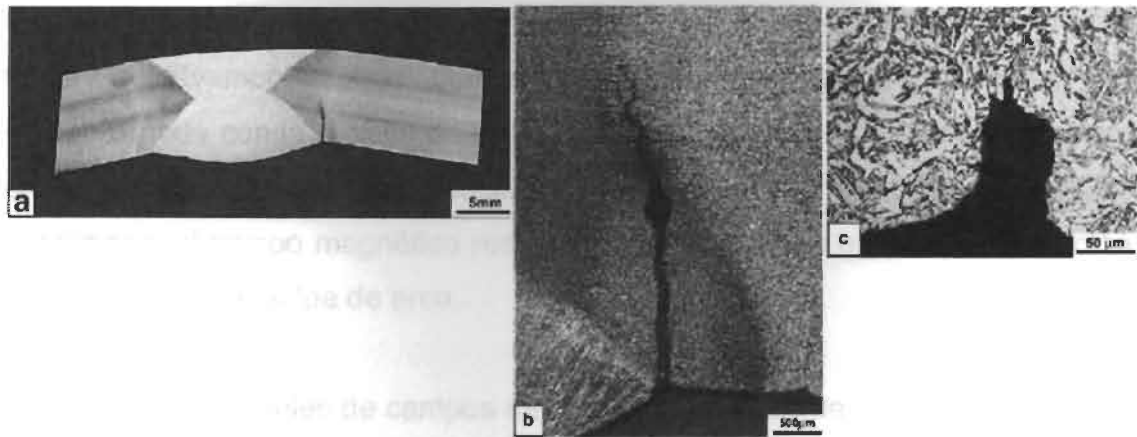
Análisis microestructural de las zonas de soldadura, ZAC y Metal base: (a) inicio del agrietamiento; (b) agrietamiento en la interface ZAC y soldadura y (c) agrietamiento asociado a defecto de soldadura ^[3].
